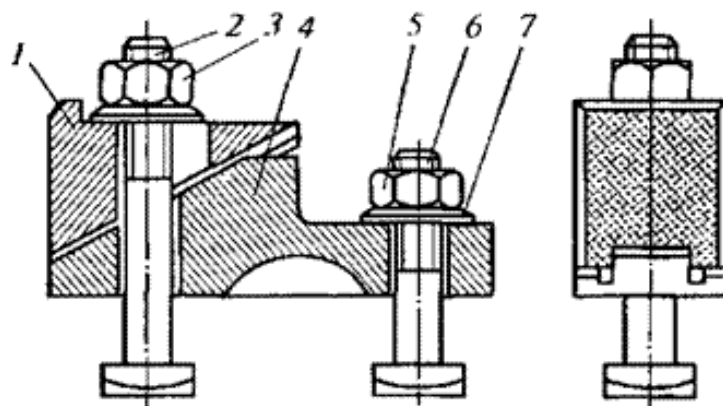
Стандартизованный клиновой зажимной механизм с ручным приводом для закрепления заготовки на столе станка:
